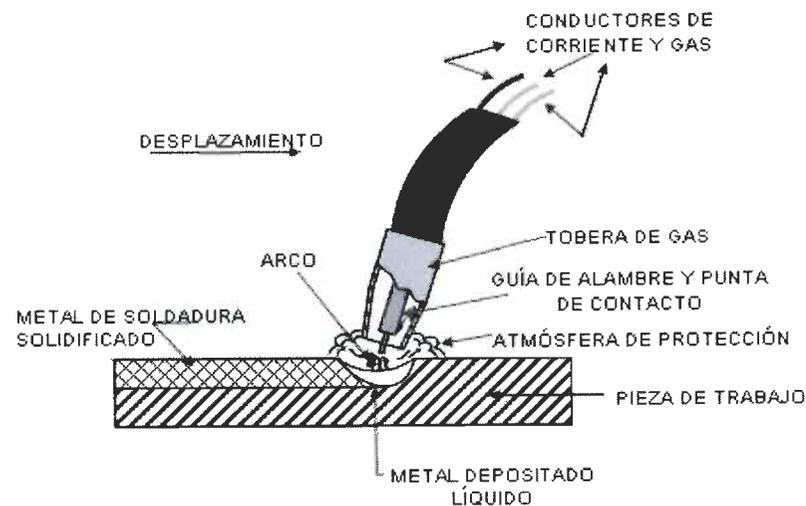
Esquema Del Proceso Soldadura GMAW
